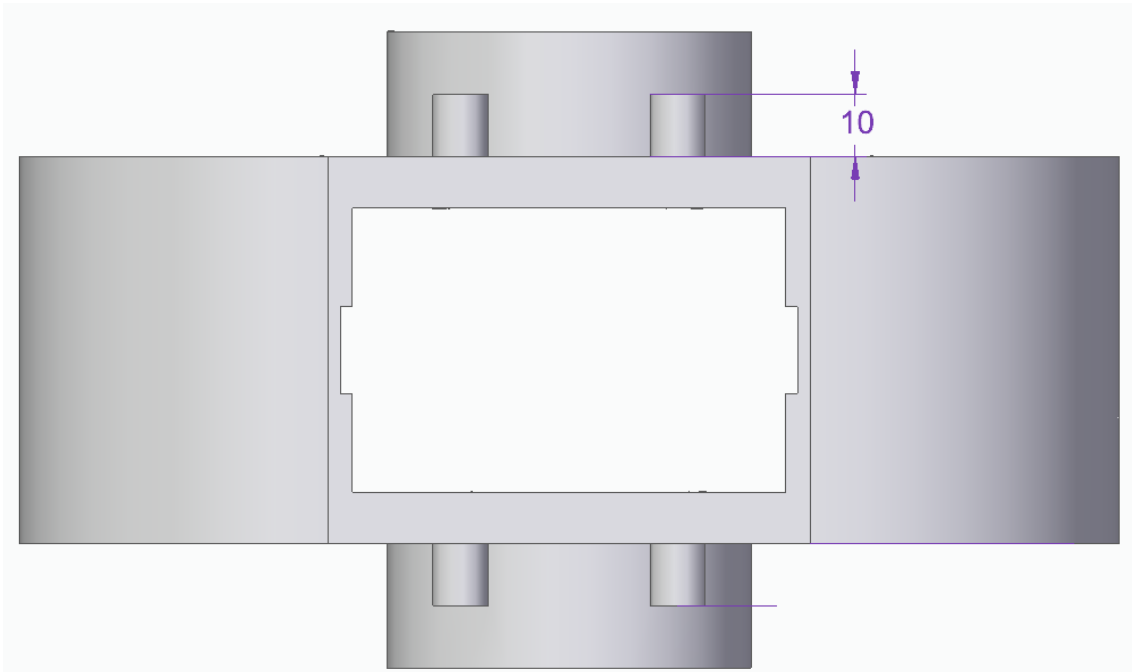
Planta de la pieza base 3. Fuente: elaboración propia
